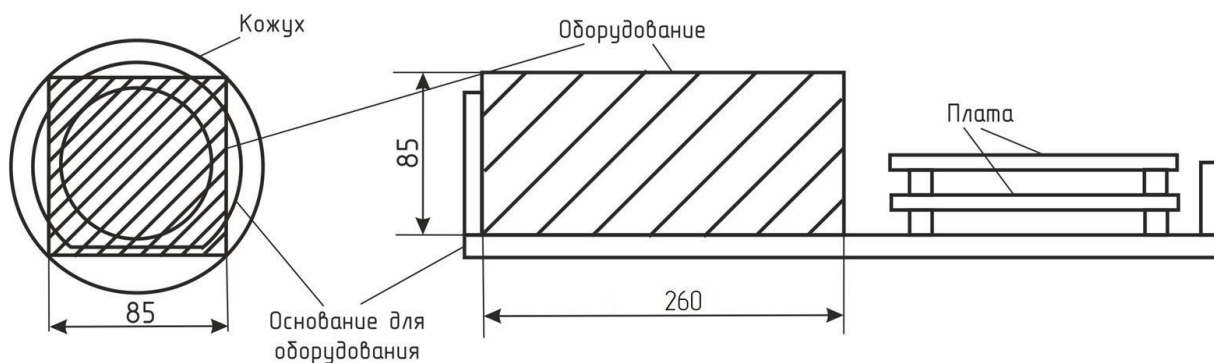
Габаритные размеры термокожуха с крепежно-юстировочным устройством
